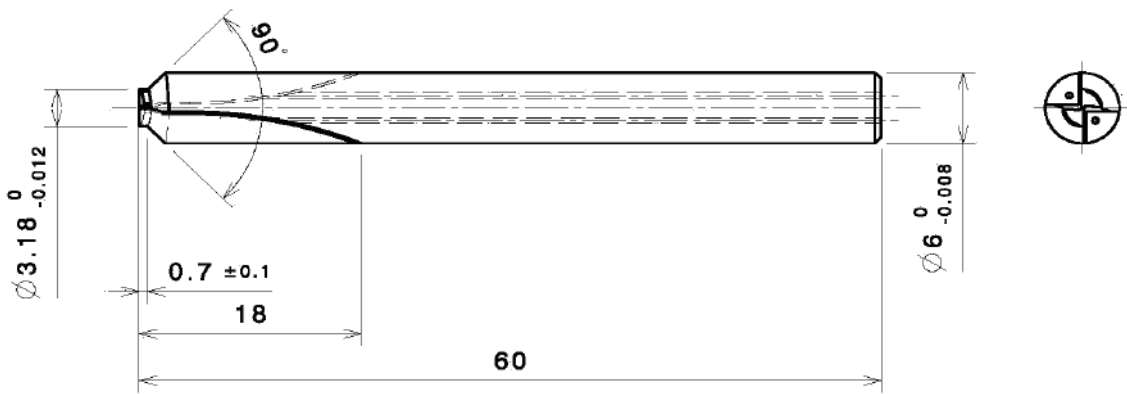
Креслення твердосплавного свердла BOF D3.18X0.7X 60-6 зі сплаву UF10
